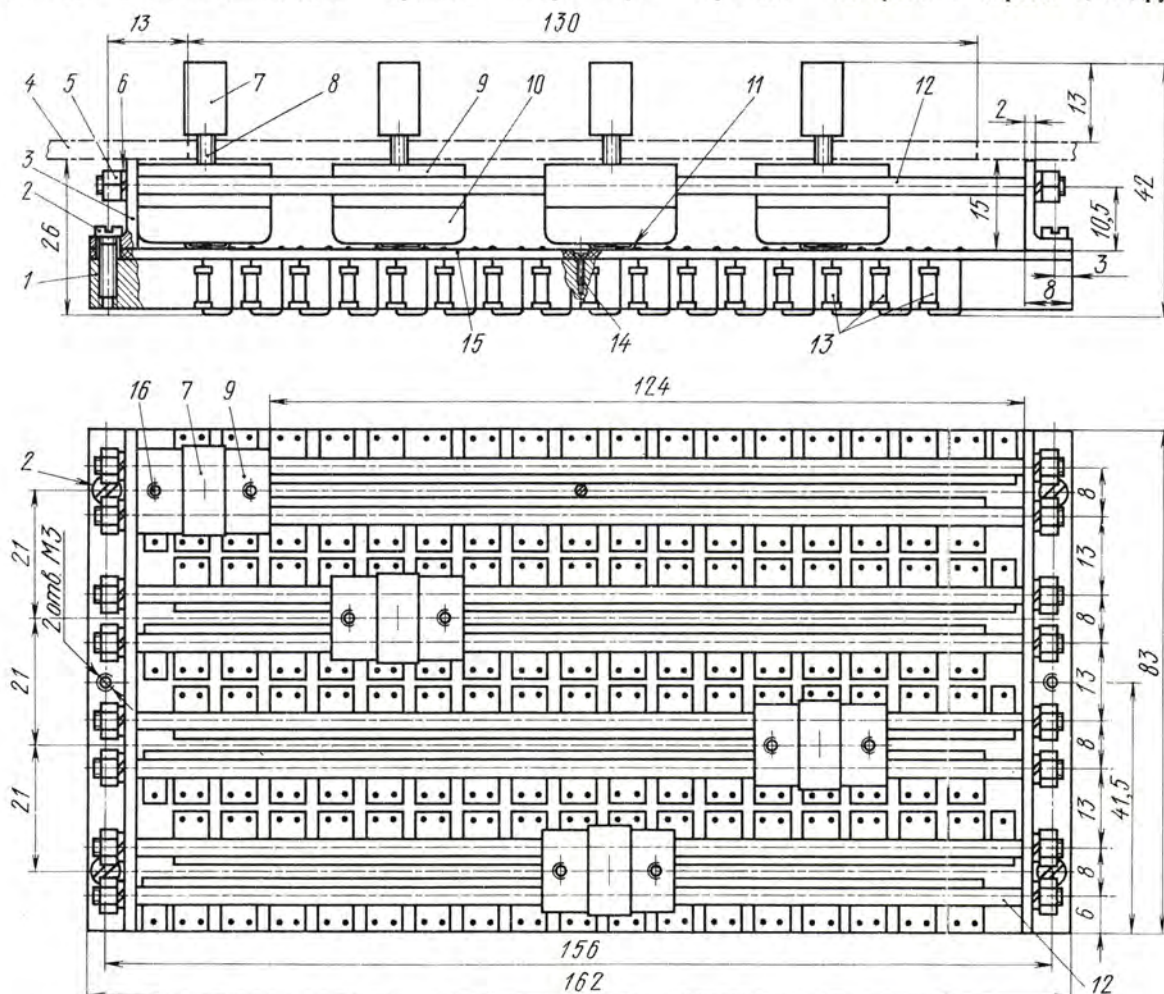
Устройство блока переменных резисторов: 1 — планка, 2 шт., закрепить на плате 15 винтами 2; 2 — винт М2,5×10, 4 шт.; 3 — уголок, Д16-Т, 2 шт., закрепить винтами 2; 4 — лицевая панель усилителя НЧ; 5 — гайка М3, 16 шт.; 6 — шайба пружинная, 16 шт.;
